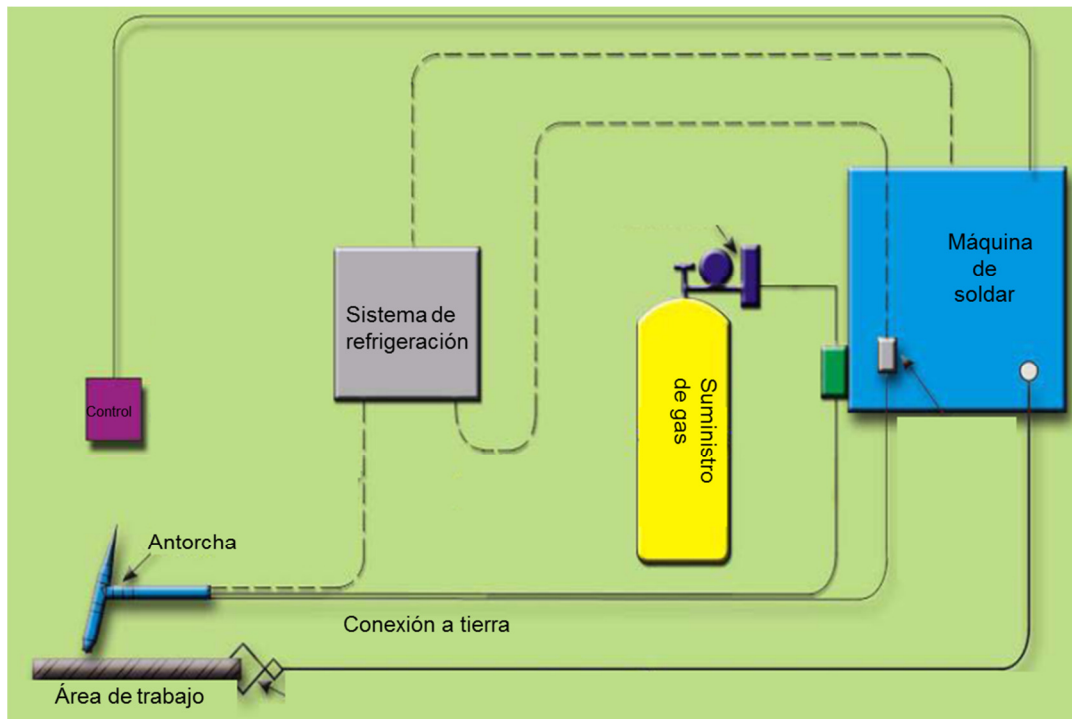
Esquema del equipo para la soldadura TIG.
